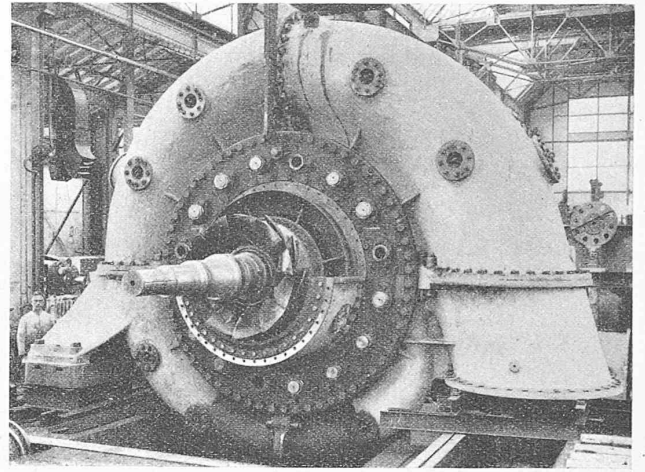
Eine der Pumpen mit 27 000 PS Kraftbedarf in den Werkstätten der A.-G. der Maschinenfabriken Escher Wyss & Cie.
